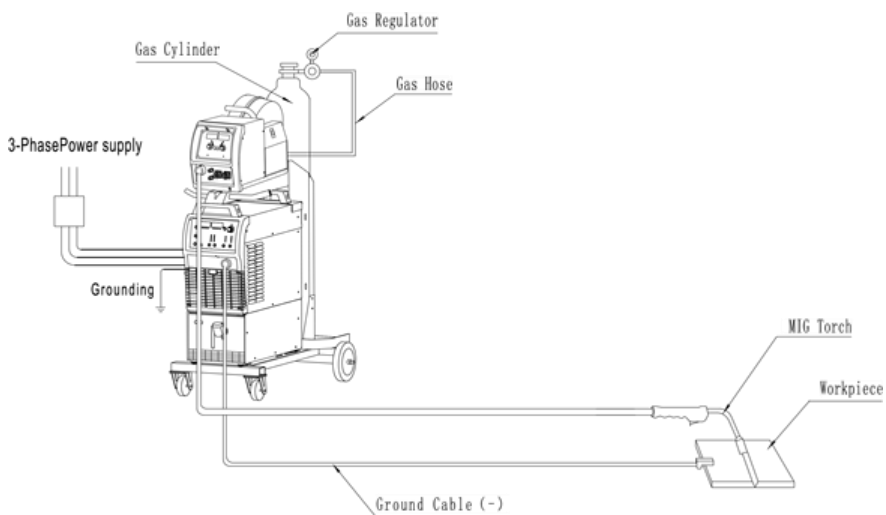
Комплект для механизированной сварки в среде защитных газов
